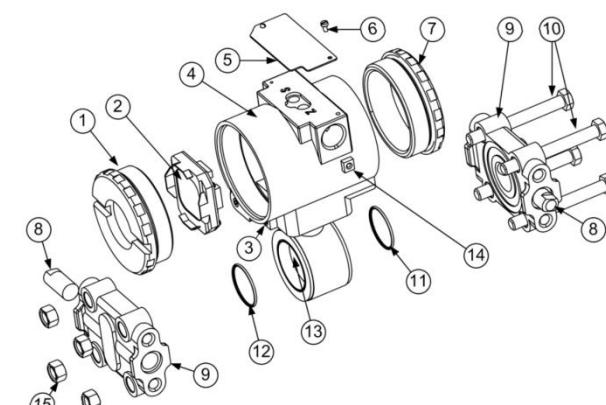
Основные элементы конструкции датчика DMD 331D.
